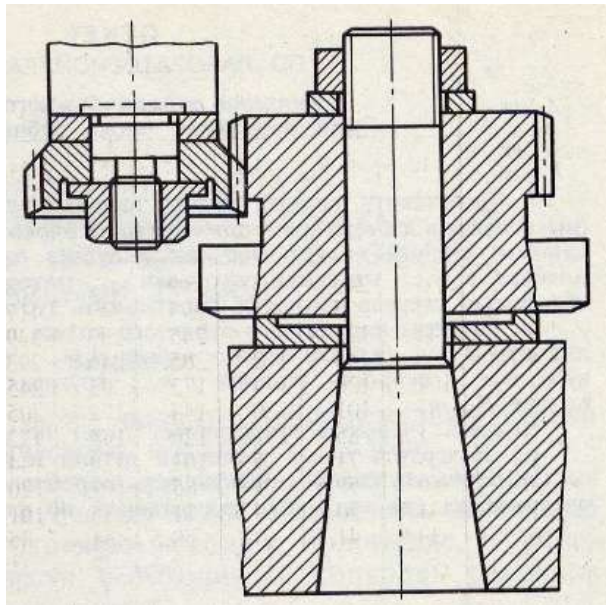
Схема установки довбала та заготовки на верстаті
